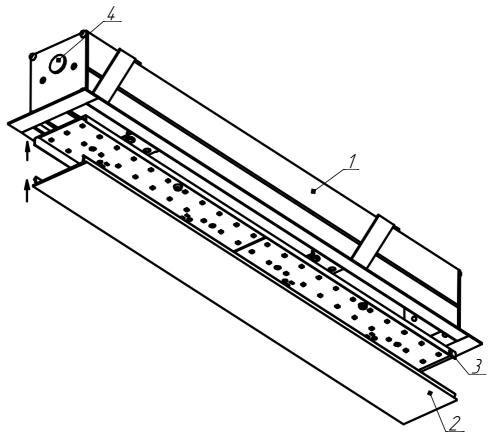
Установка панели и рассеивателя в светильник ДВО02 1 - корпус светильника; 2 - рассеиватель; 3 - панель; 4 - крышка торцевая ДВО02.
